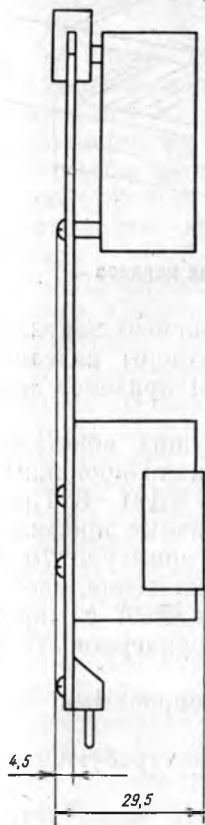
Сборочный чертеж ячейки стабилизатора
